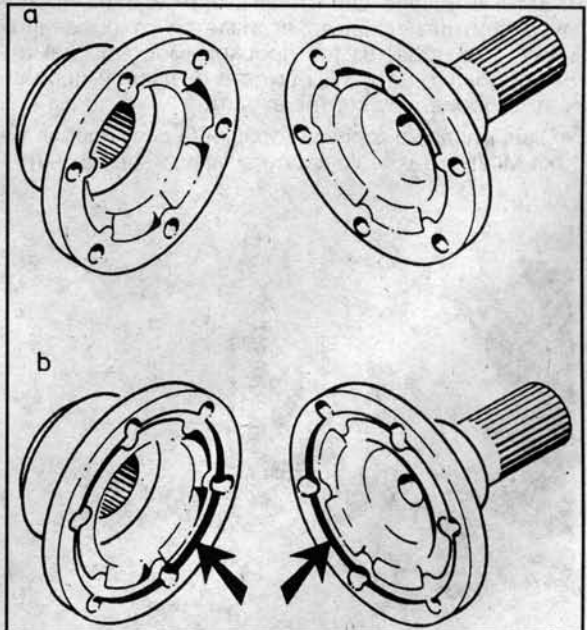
Фланцы приводных полуосей без канавки на лицевой поверхности (а) и с канавками (б)
